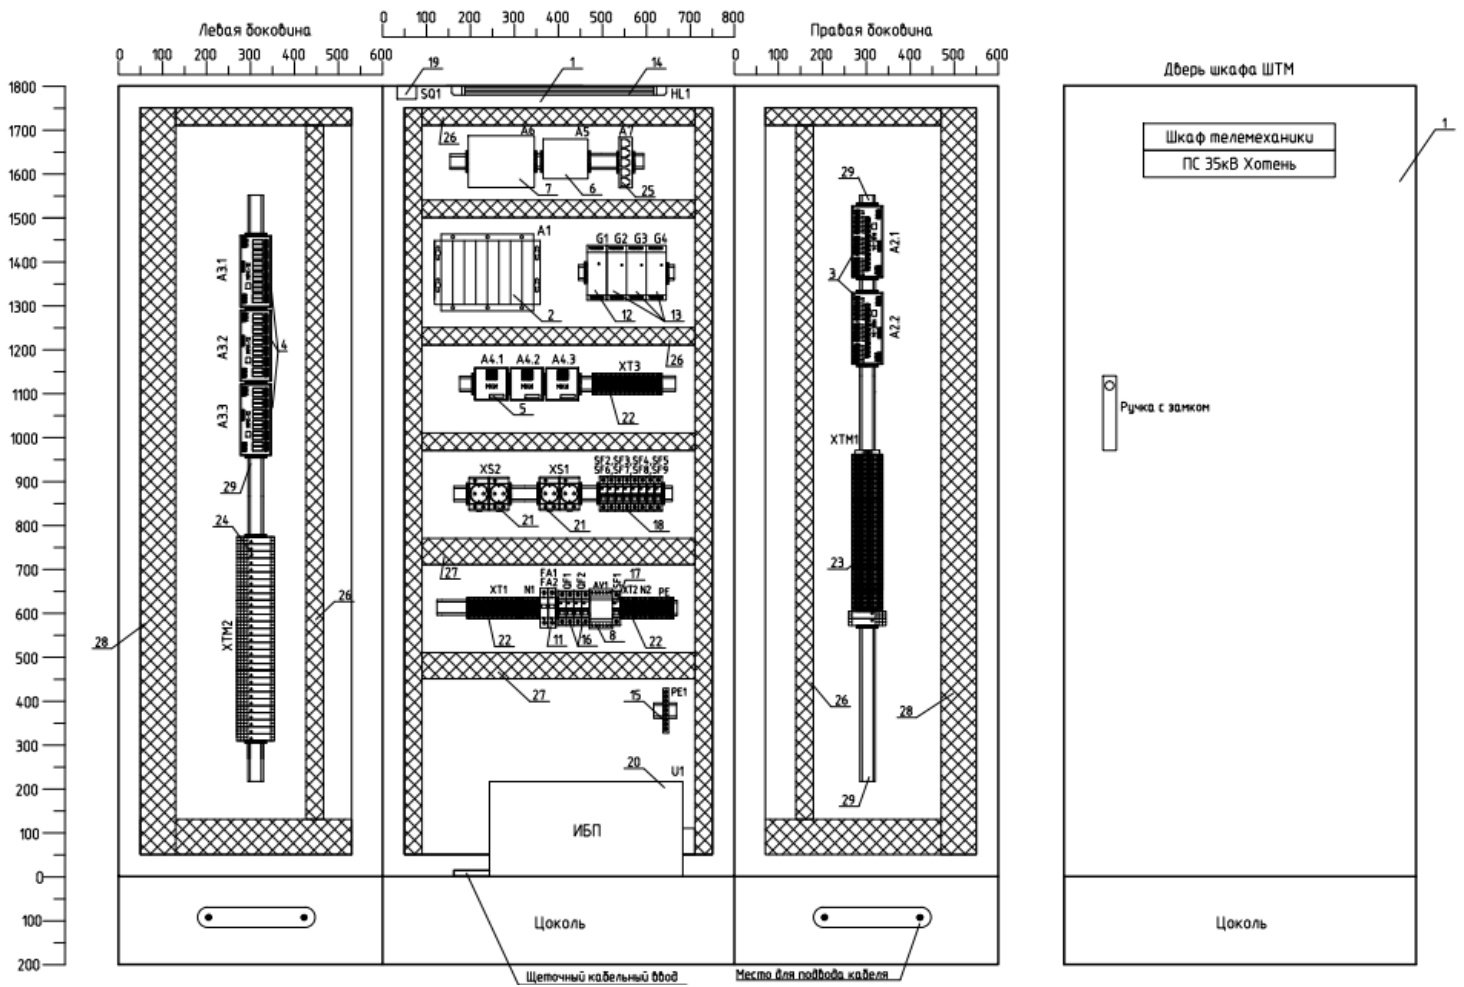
Общий вид и габаритные размеры ШТМ.
